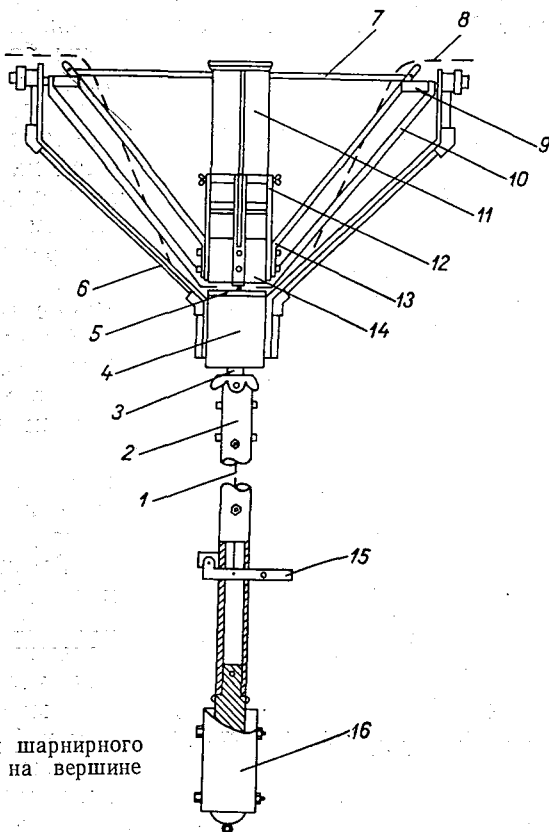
Устройство для шарнирного крепления осадкомера на вершине мачты.
